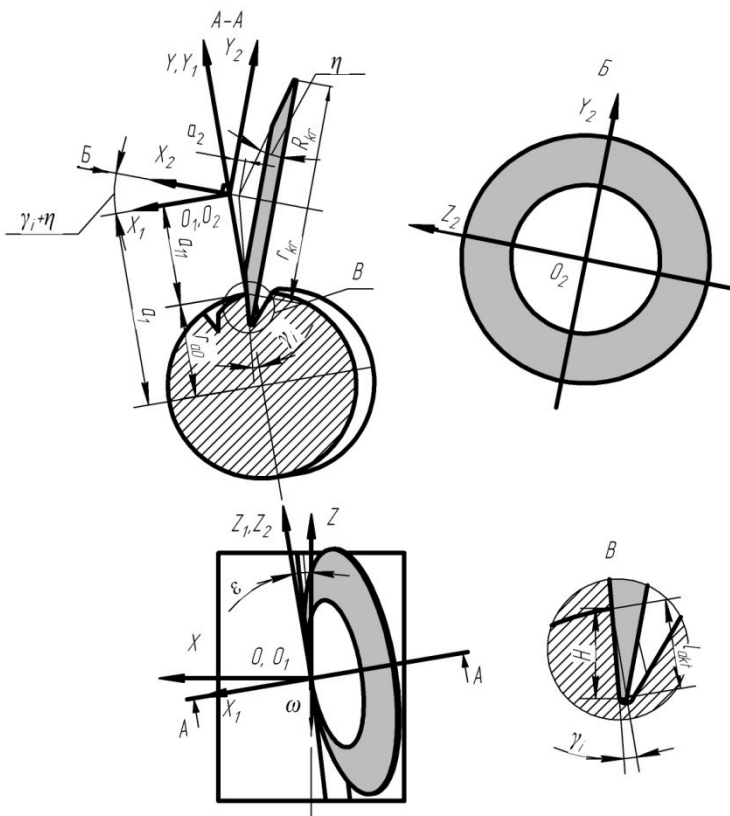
Установка заточувального круга при утворенні передньої гвинтової поверхні зуба фрези
